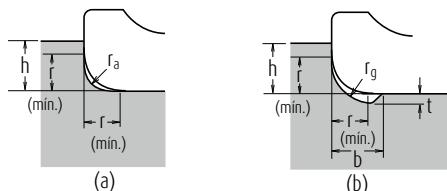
2 Dimensiones del Chaflán y Altura de Codo
